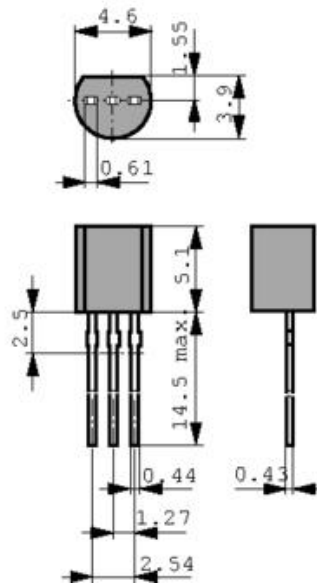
Габаритні розміри корпусу напівпровідникових елементів TO-92
